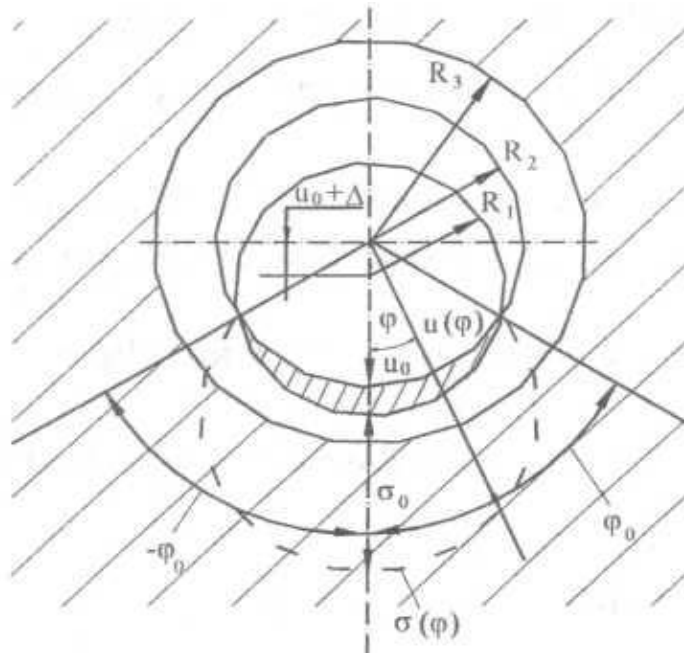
Розрахункова схема підшипника ковзання :
